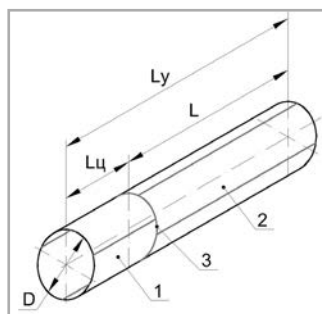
Схема сварной удлиненной обечайки котла железнодорожной вагон-цистерны, изготовленной по комбинированной технологии: 1 – дополнительная царга; 2 – штатная обечайка; 3 – кольцевой сварной шов; L – длина штатной обечайки;  $L_c$  – длина дополнительной царги;  $L_y$  – длина удлиненной обечайки.
